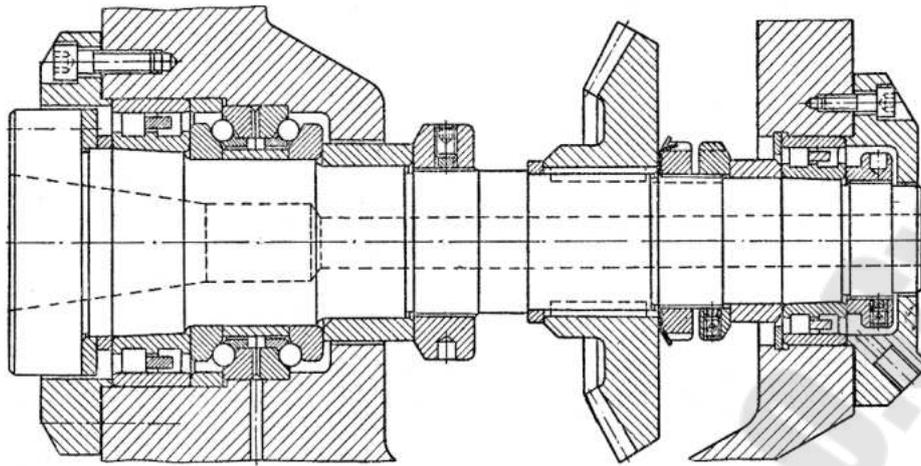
Шпиндельный узел фрезерного станка с упорно-радиальными шарикоподшипниками
